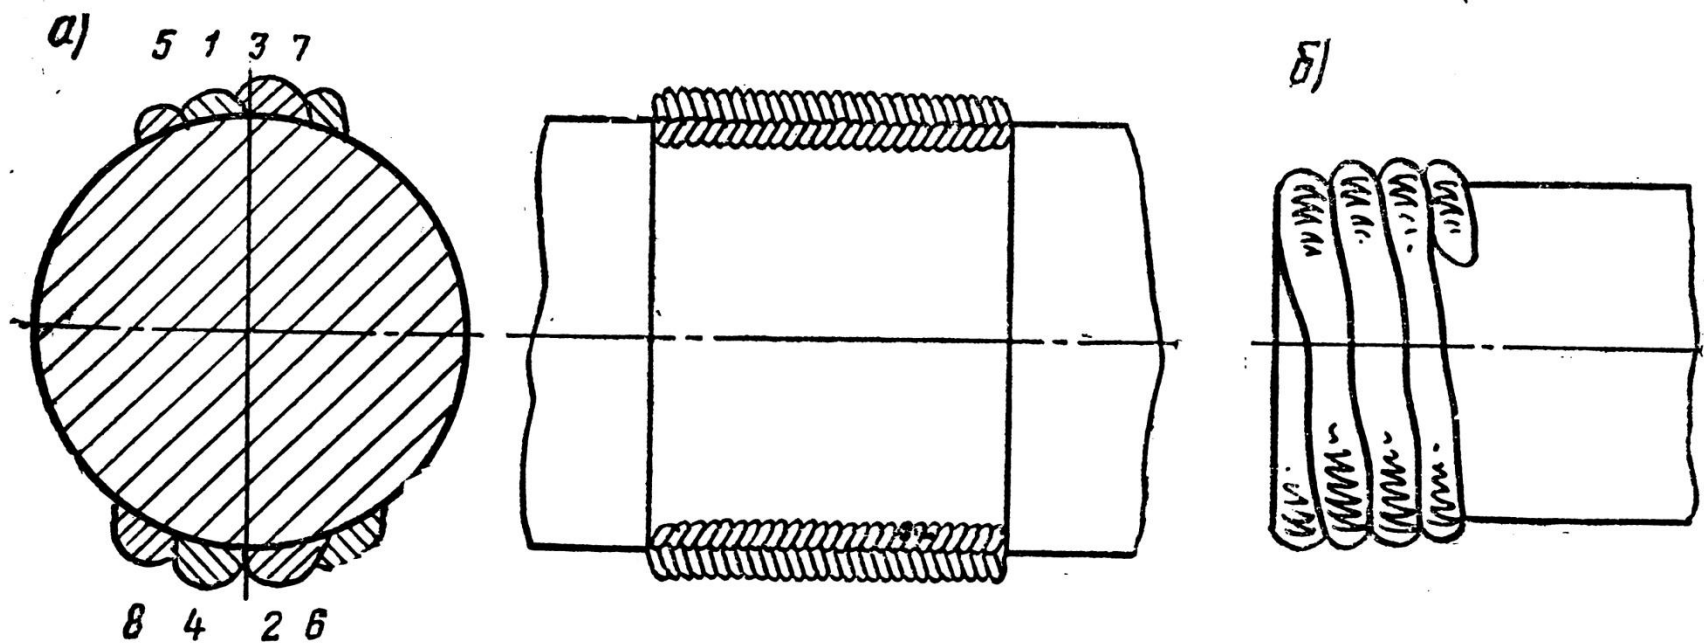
Последовательность наплавки металла на изношенный вал:
